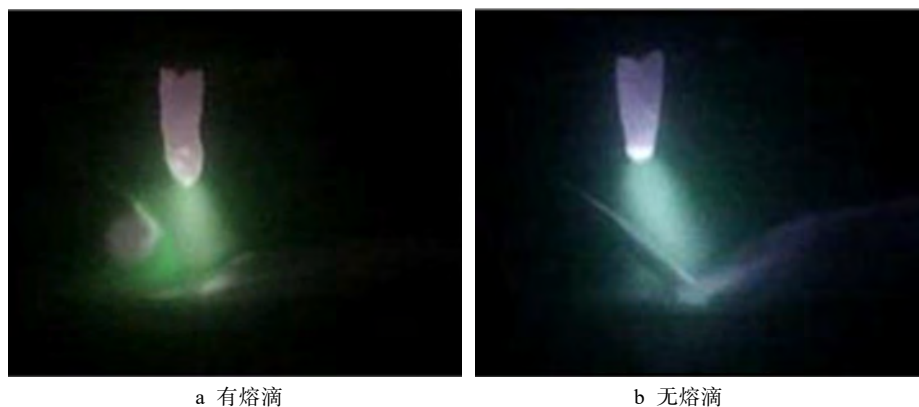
耦合电弧预热焊丝 GTAW 焊两种熔滴过渡形式
